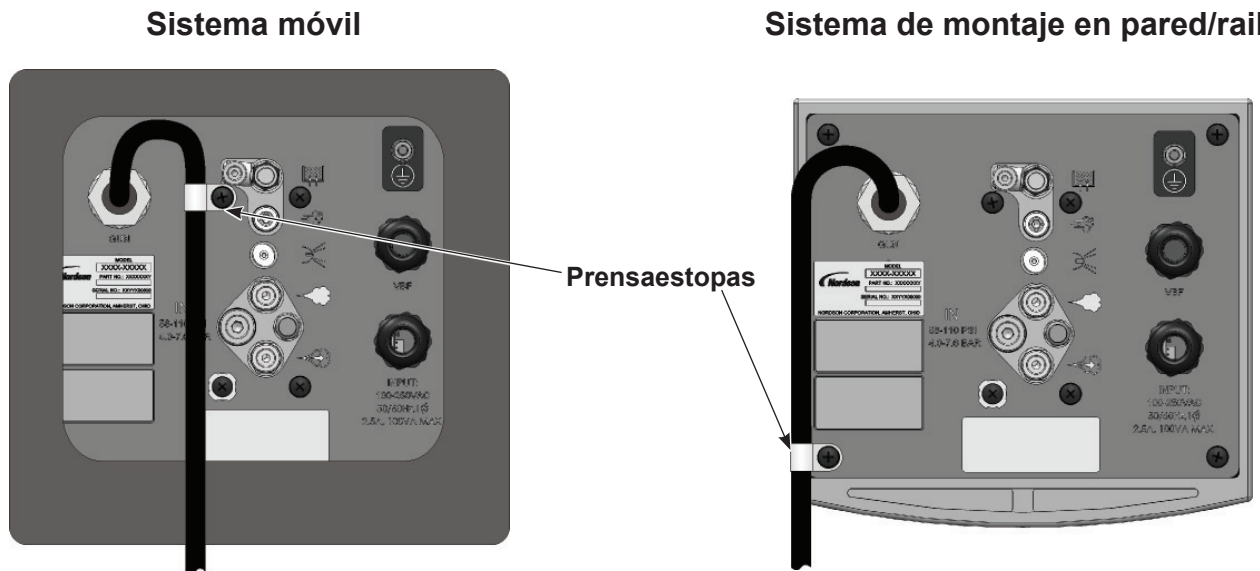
Conexión del cable de la pistola y montaje del prensaestopas
